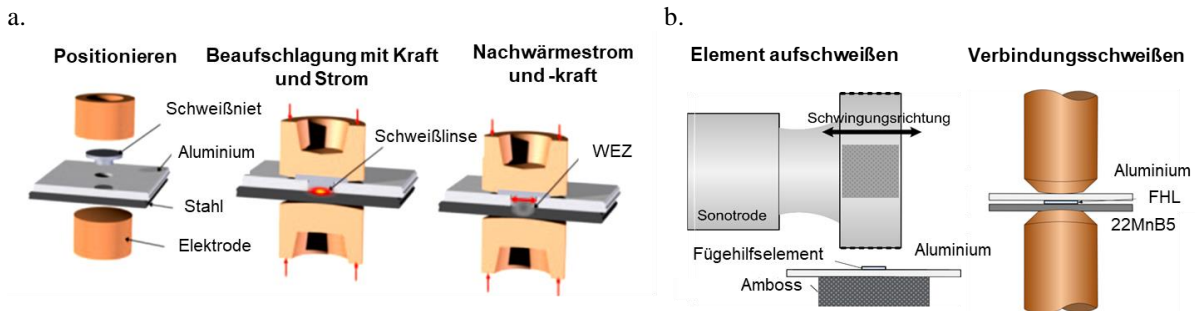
a. Verfahrensablauf des Widerstandselementschweißens [12] und b. Ultraschall-Widerstandspunktschweißens mit dem Fügehilfselement, nach [13]
